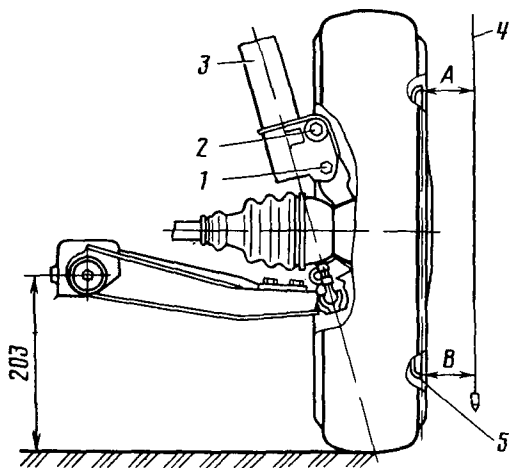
Проверка и регулировка угла развала переднего колеса:
